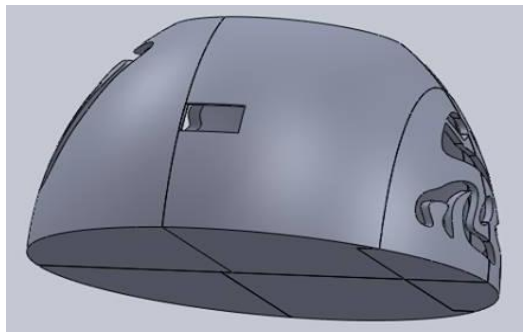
Parte superior del tronco del robot diseñado en SolidWorks
